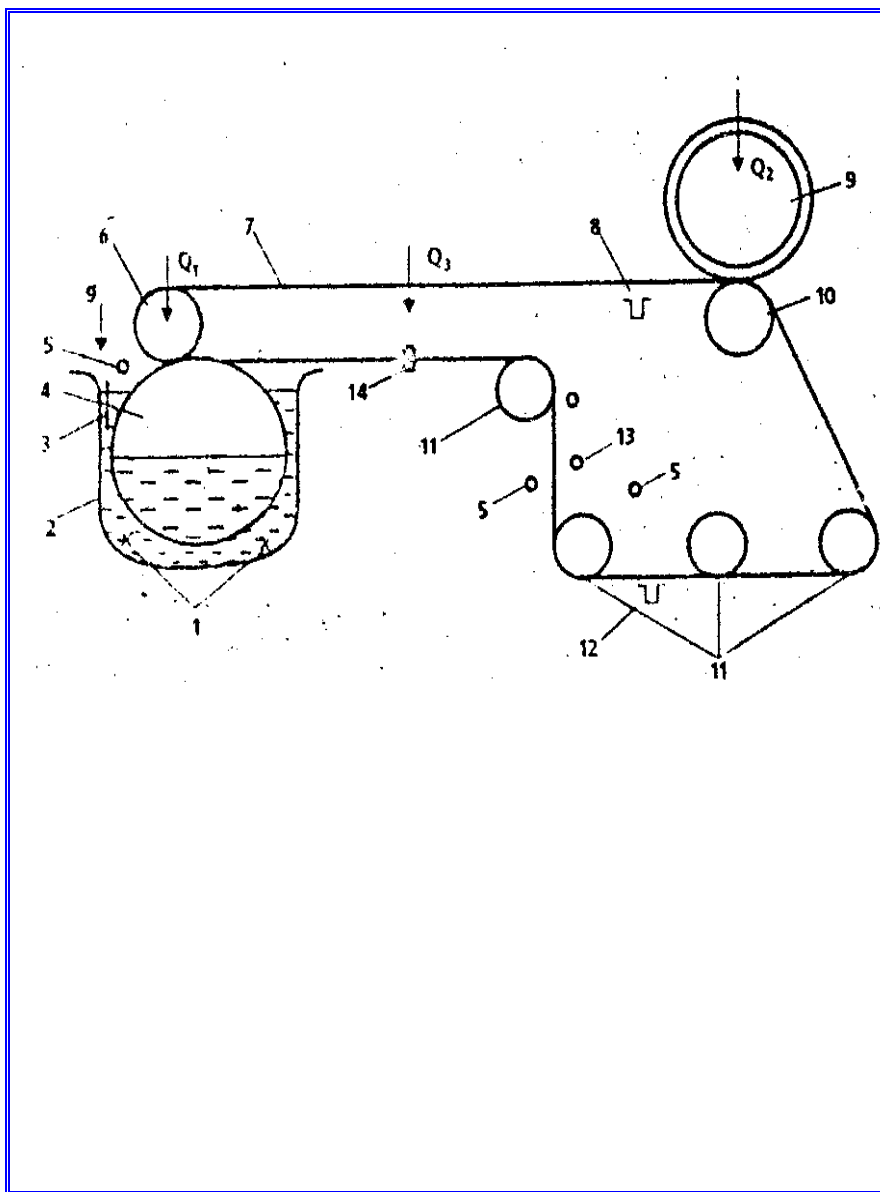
11.3.Схема формувальної машини для виробництва азбестоцементу: 1 – змішувач; 2 – ванна; 3 – перегородка; 4 – сітчастий циліндр; 5 – промивні труби; 6 – вал; 7 – суконна стрічка; 8,12 – вакуум-коробки; 9 – металевий форматний циліндр; 10 – ведучий вал; 11 – напрямні валки; 13 – відбійний валик; 14 – віджимні валки
